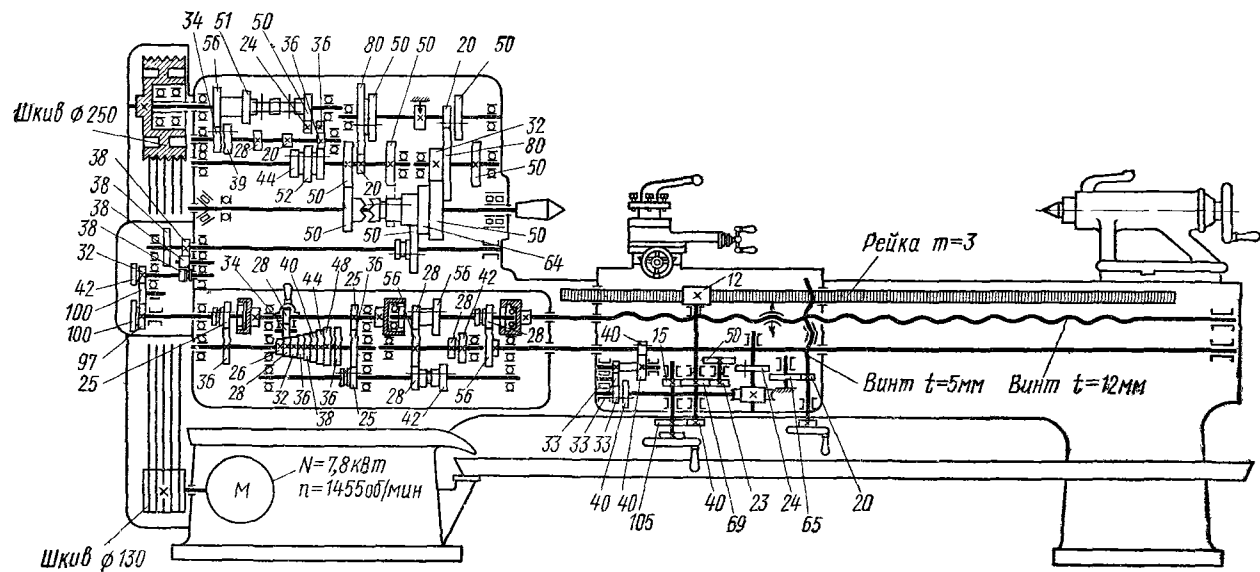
Кинематическая схема станка 1А62 (цифрами обозначены числа зубьев)
